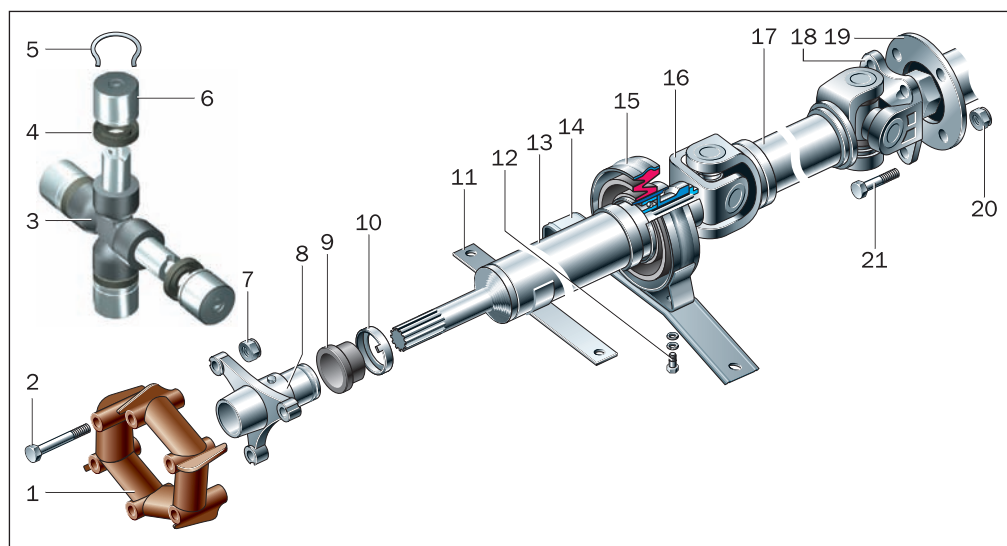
Карданная передача: 1 — эластичная муфта; 2 — болт крепления эластичной муфты к фланцу; 3 — крестовина; 4 — сальник; 5 — стопорное кольцо; 6 — подшипник крестовины; 7 — гайка; 8 — фланец эластичной муфты; 9 — сальник; 10 — обойма сальника; 11 — кронштейн безопасности; 12 — болт крепления кронштейна к промежуточной опоре; 13 — передний карданный вал; 14 — кронштейн промежуточной опоры; 15 — промежуточная опора; 16 — вилка переднего карданного вала; 17 — задний карданный вал; 18 — вилка заднего карданного вала; 19 — фланец ведущей шестерни главной передачи; 20 — гайка; 21 — болт крепления вилки
